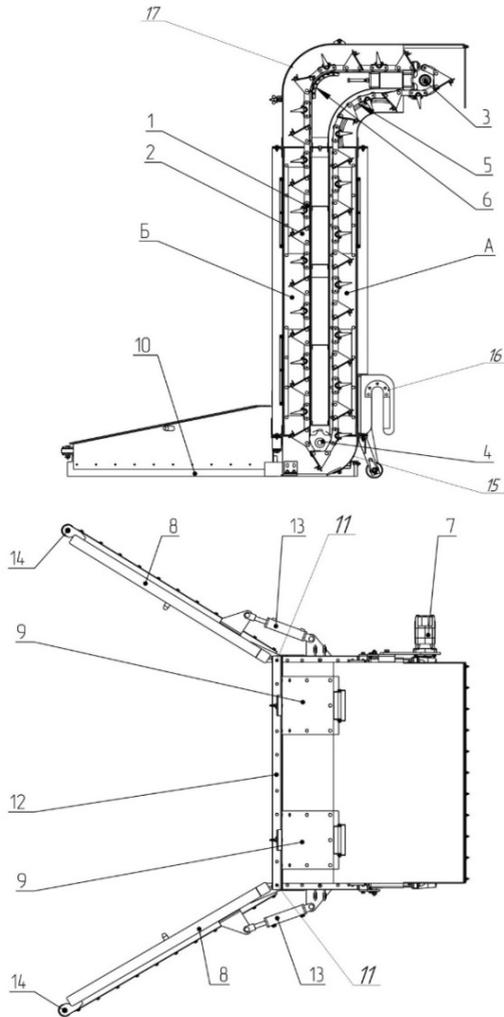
Скрепер-элеватор в разрезе и вид сверху:
